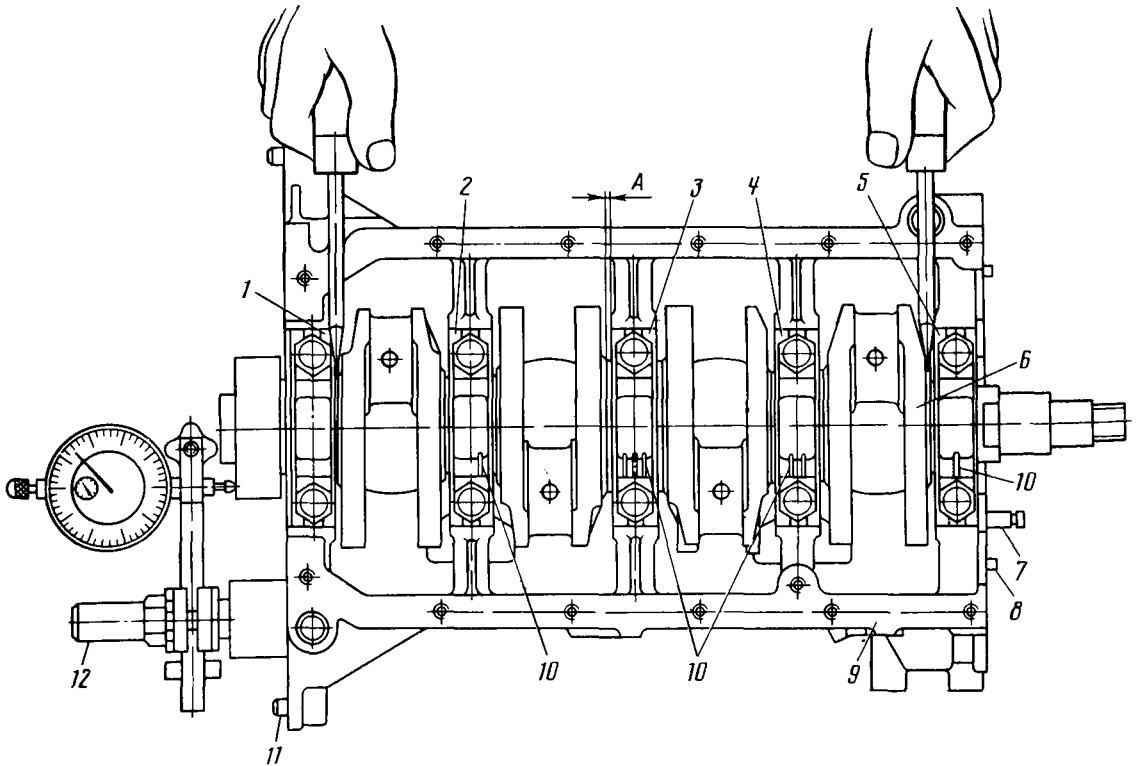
Проверка осевого разбега и маркировка крышек подшипников коленчатого вала:
